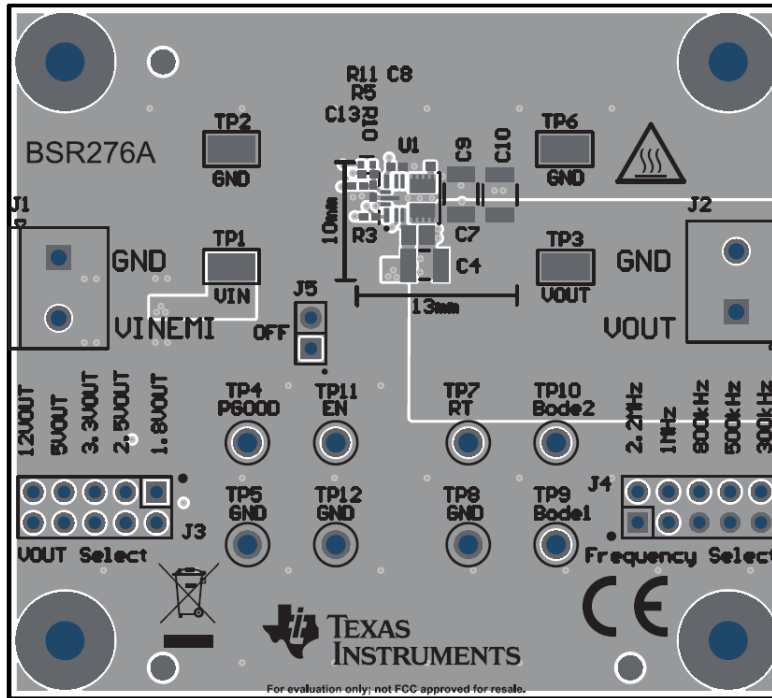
PCB 顶层 2D (TPSM365R15EVM)
